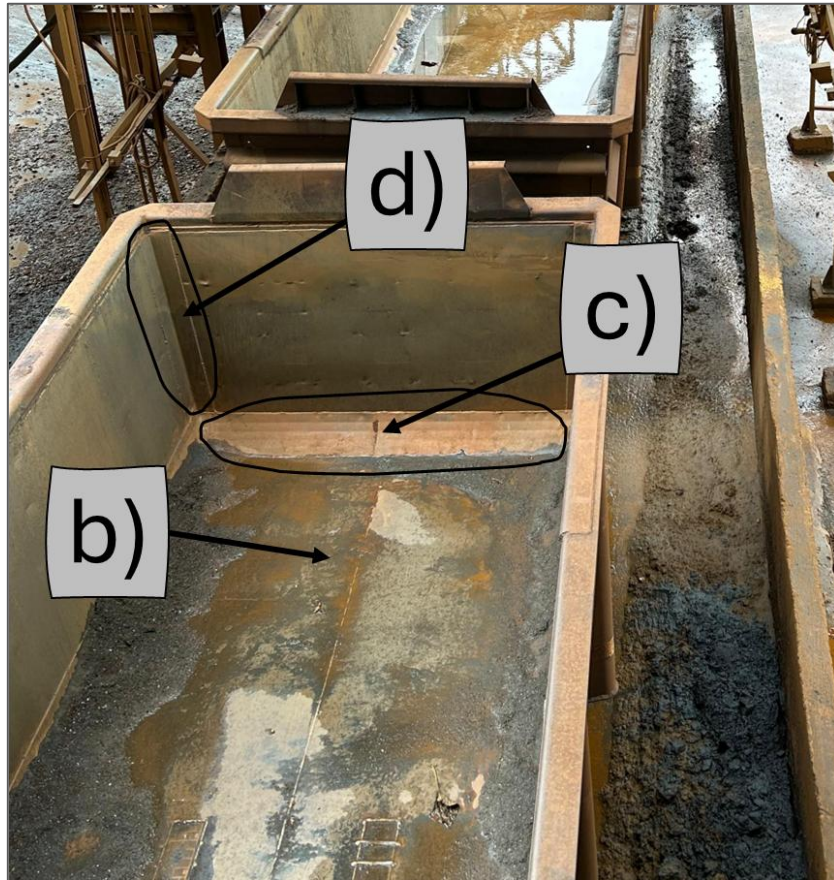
Junções internas críticas do vagão para formação de recheio: b) chapa plana; c) chapa fletida em um raio de 250mm e d) chapas soldadas em 90°.
